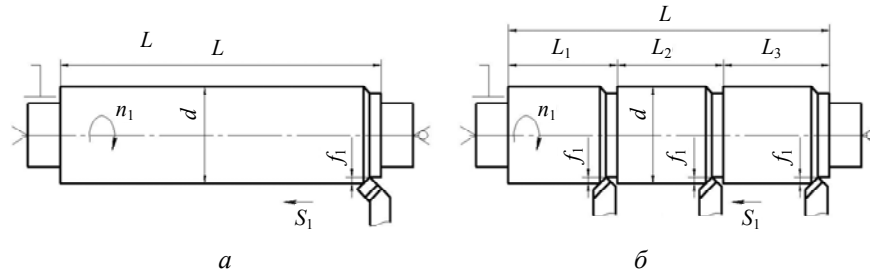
Схемы обработка вала: а — однорезцовая; б — многорезцовая
